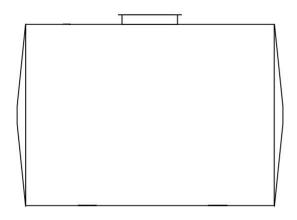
Эскиз резервуара РГС-5 зав.№ 17
